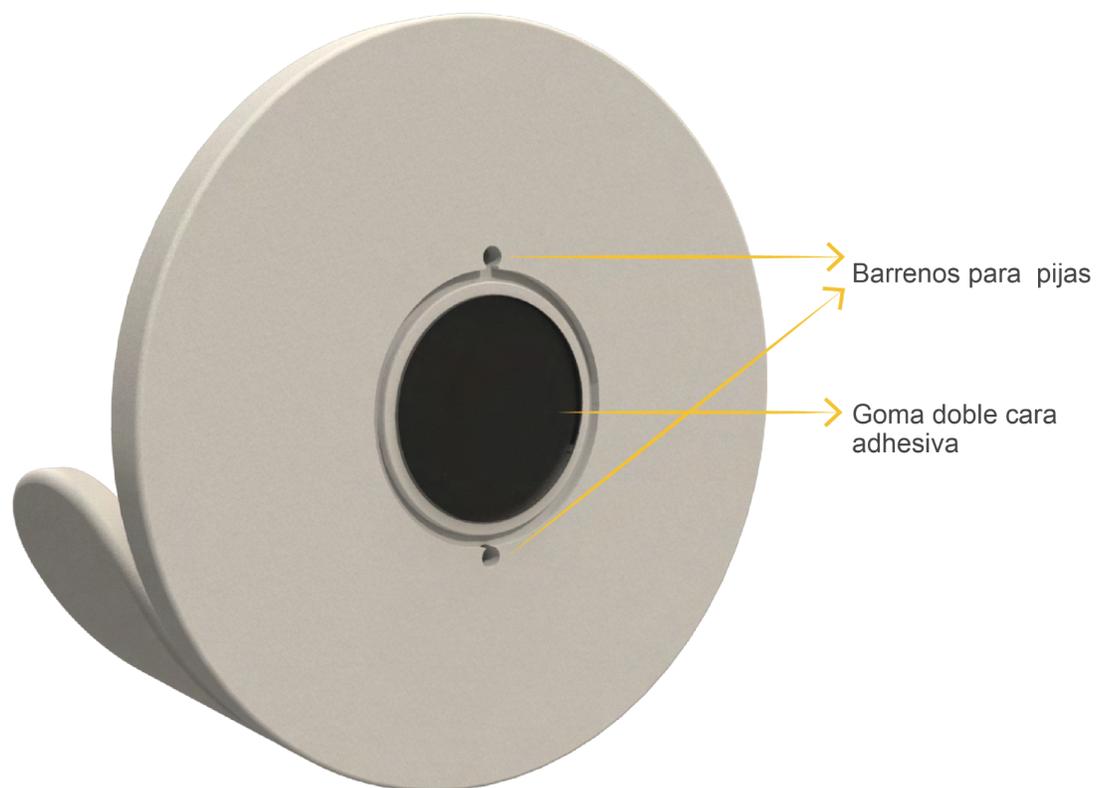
Vista posterior de la carcasa fija que muestra la goma doble cara adhesiva y los barrenos para la sujeción al muro.
